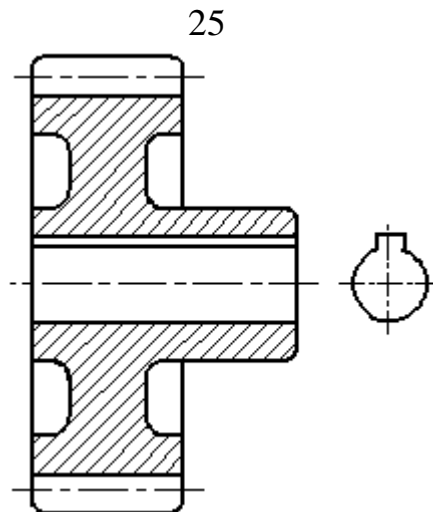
Образец изображения отверстия в ступице зубчатого колеса.
